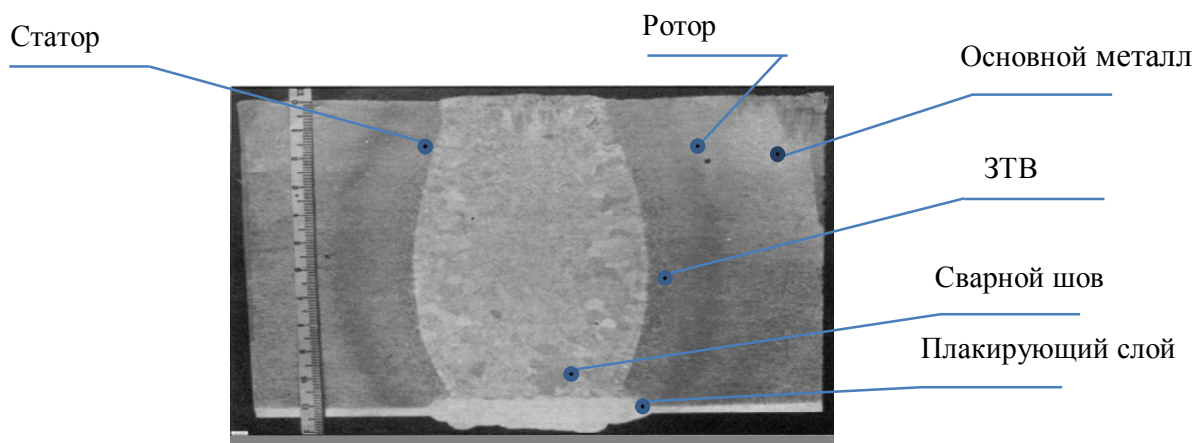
Макрошлиф сварного соединения биметалла Вст3 +10X13
